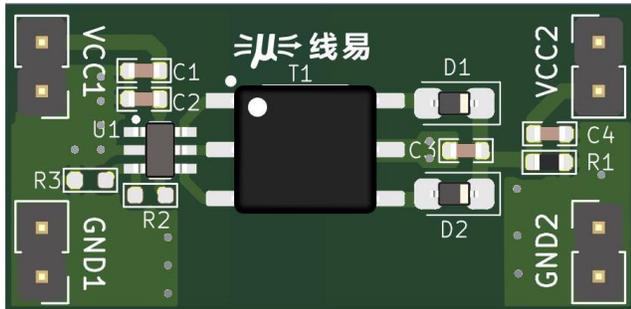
PCB 版图正面 (尺寸: 16 x 33mm)
